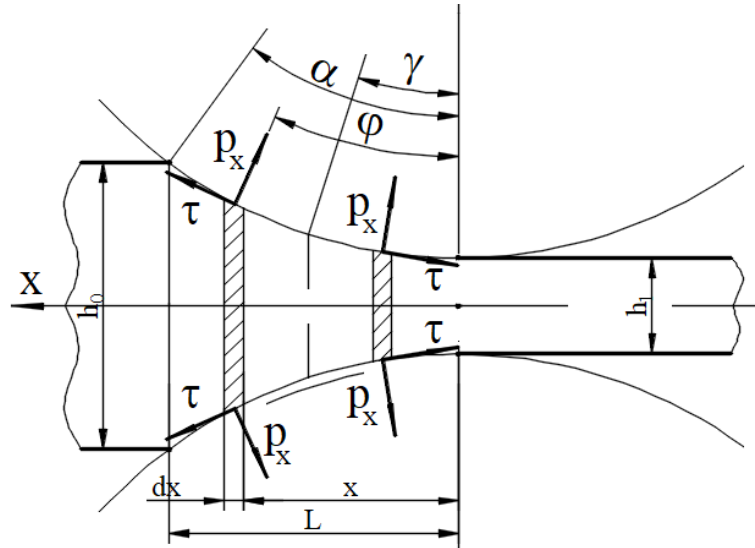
Розрахункова схема для визначення тиску металу на валки
